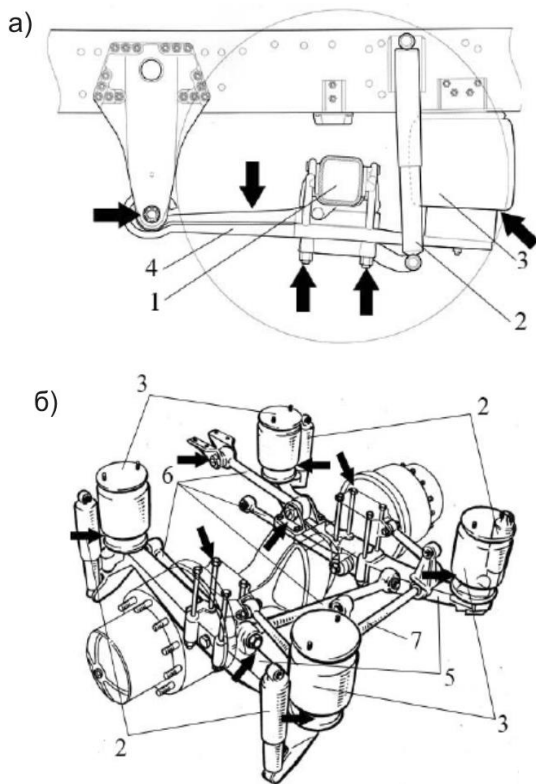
Варианты исполнения пневмоподвесок неуправляемых осей и основные места их контроля: *а* – с одной пневморессорой на колесо; *б* – с двумя пневморессорами на колесо; 1 – пневморессора; 2 – амортизатор; 3 – балка оси; 4 – полурессора; 5 – реактивные тяги; 6 – стабилизатор; 7 – опорные кронштейны.
